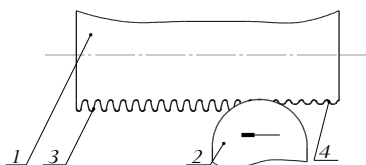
Схема вигладжування поверхні заготовки під час ЕМО:
